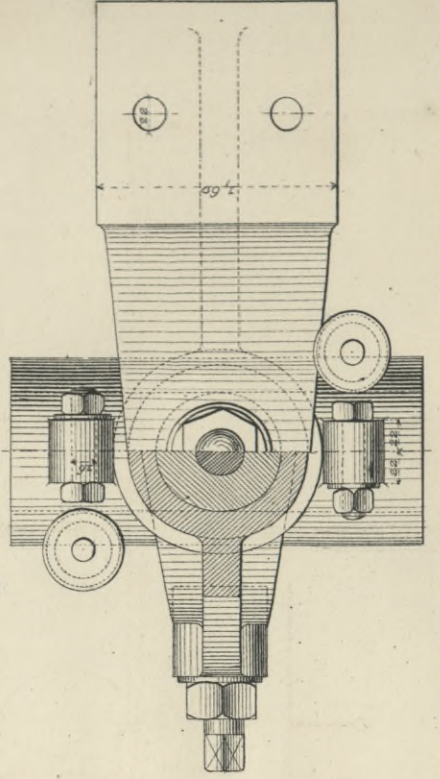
Plan et Coupe à 0^m.20 pour 1^m.
